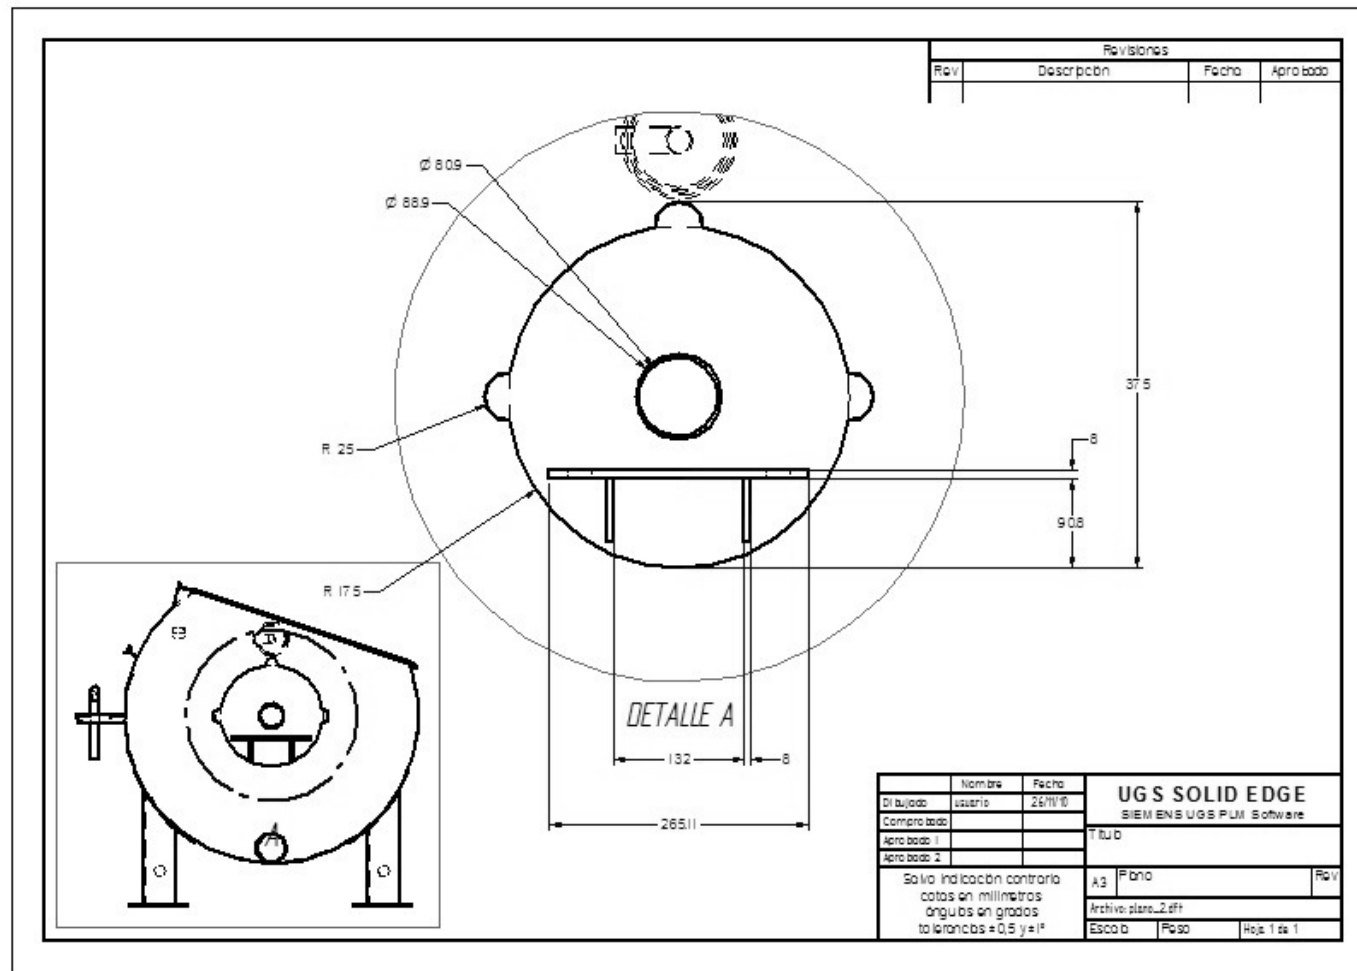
Plano del contenedor de mezclado, vista izquierda, detalle 2.
